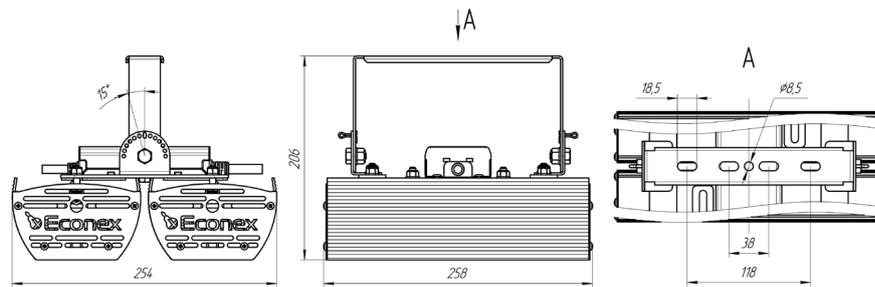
Габаритный чертеж светильника Kvant 100 G3
